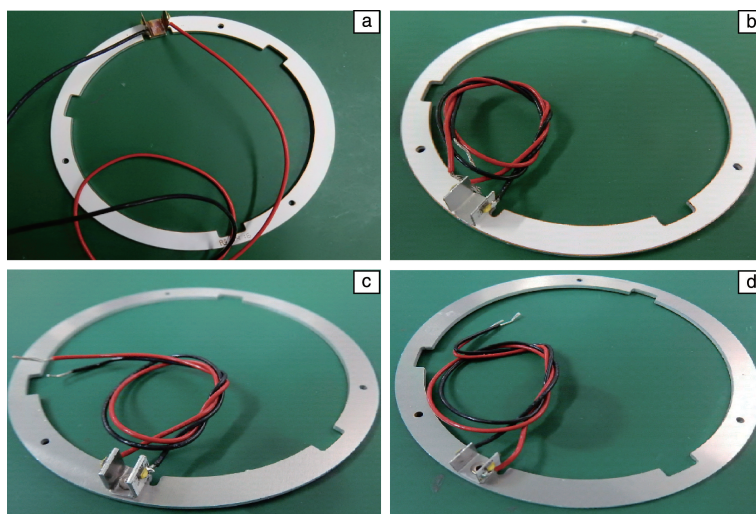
天使眼散热方案：(a)0.4 mm 厚热电分离式 MCPCB 焊接方案，(b)0.3 mm 厚普通 MCPCB 焊接方案，(c)1.0 mm 厚普通 MCPCB 铆接方案，(d)0.3 mm 厚普通 MCPCB 铆接方案
